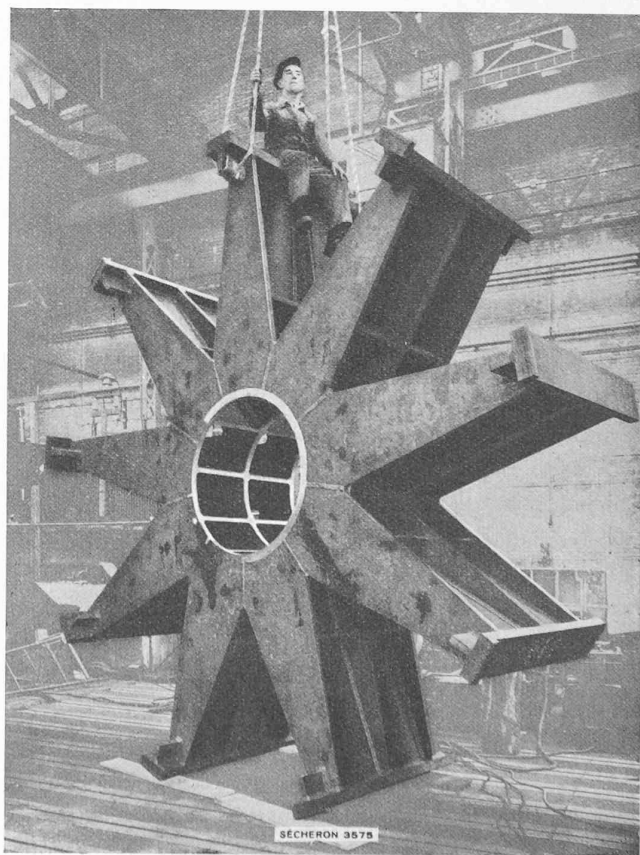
Croisillon soudé de la roue polaire des alternateurs du Verbois.
